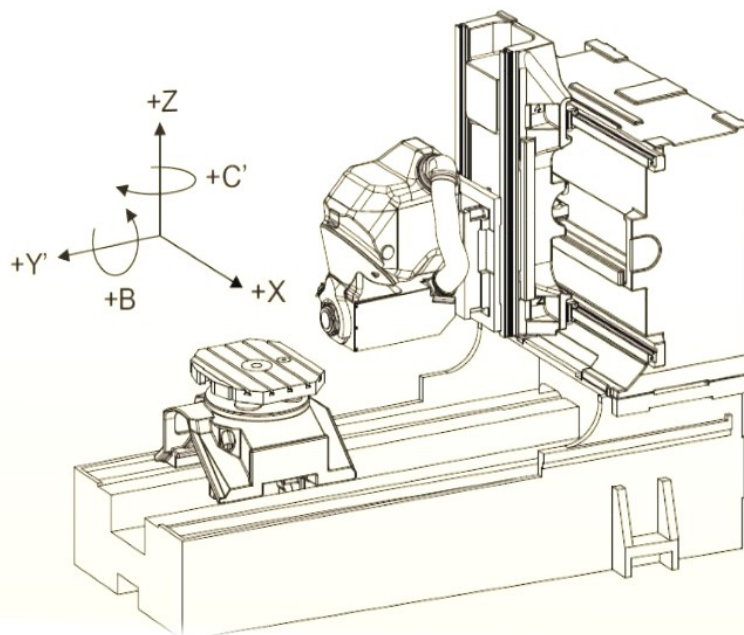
Компоновка станка DMU-80 P duoBLOCK
